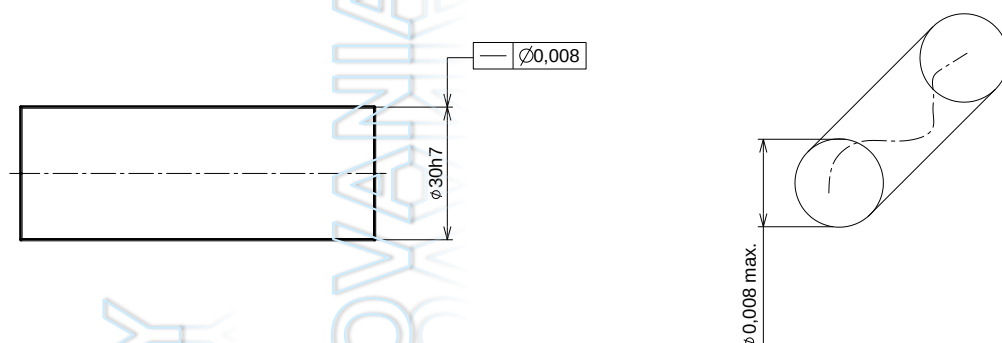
Tolerancia priamosti v rovine – príklad
